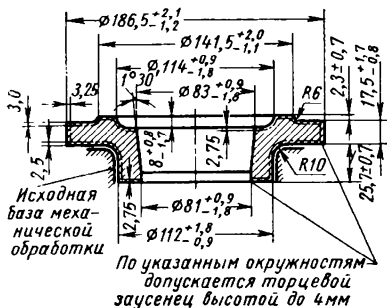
Форма и размеры поковки фланца с начисленными припусками и допусками
